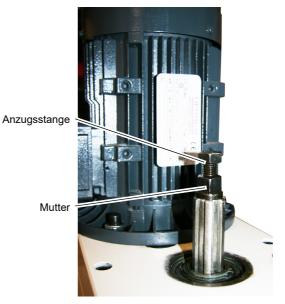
Bohr- Fräskopf ohne Abdeckkappe Anzugsstange
